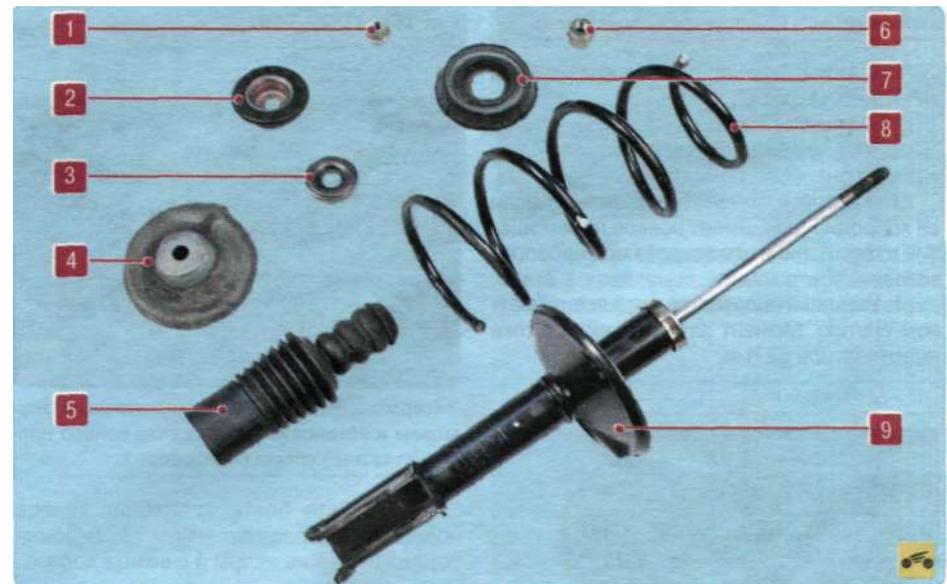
Детали амортизаторной стойки: 1 - гайка верхнего крепления амортизаторной стойки; 2 - верхняя подушка; 3 - опорный подшипник; 4 - верхняя тарелка пружины; 5 - буфер сжатия с защитным чехлом; 6 - гайка штока амортизатора; 7 - верхняя опора стойки; 8 - пружина; 9 - амортизатор
